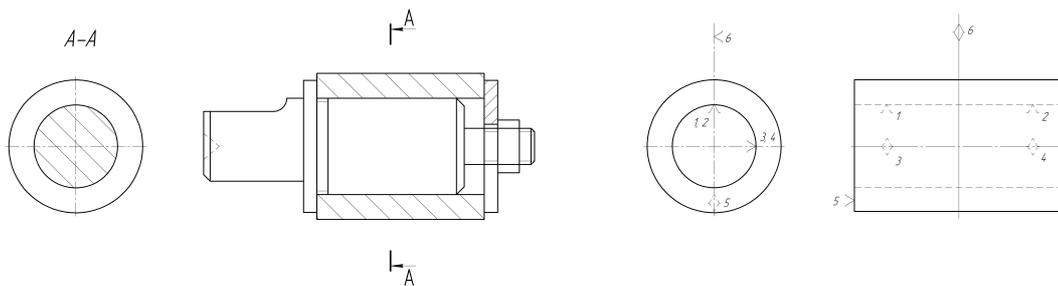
Установка втулки на цилиндрической оправке (с зазором):
